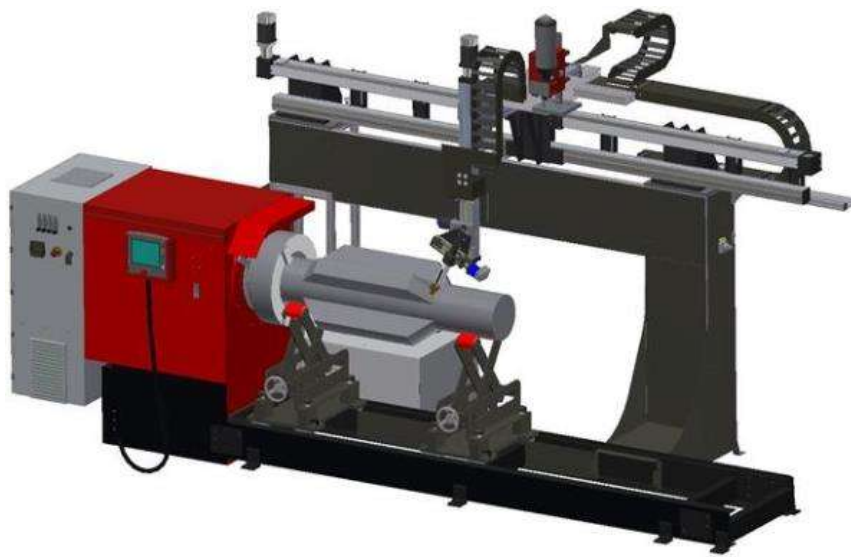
Установка універсальна CWD 1000-3000 [23]
